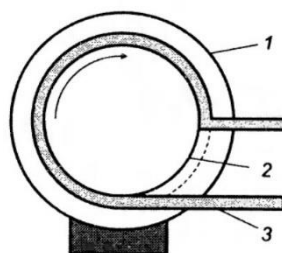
Схема процесса РКУП-К: 1 – ограничительная оснастка; 2 – вращающийся центральный вал; 3 – заготовка [14]
